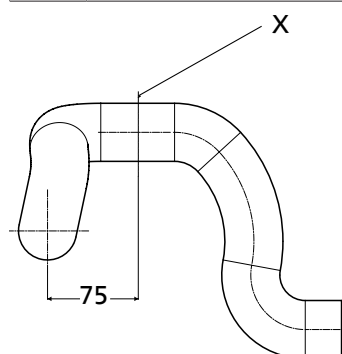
Шланг при напорном патрубке справа, размеры [мм]
